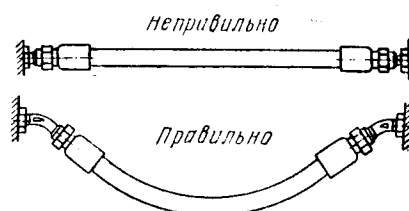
Схема монтажа шланга без натяжения.
